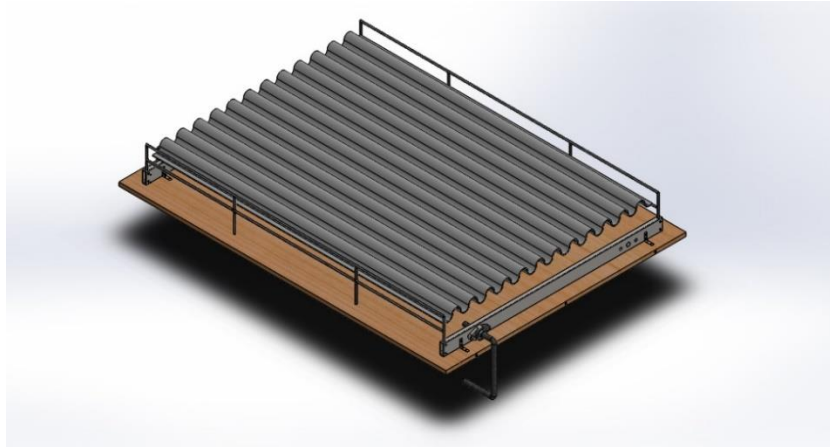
Colocación del soporte ondulado en el subsistema de cama plegable.
